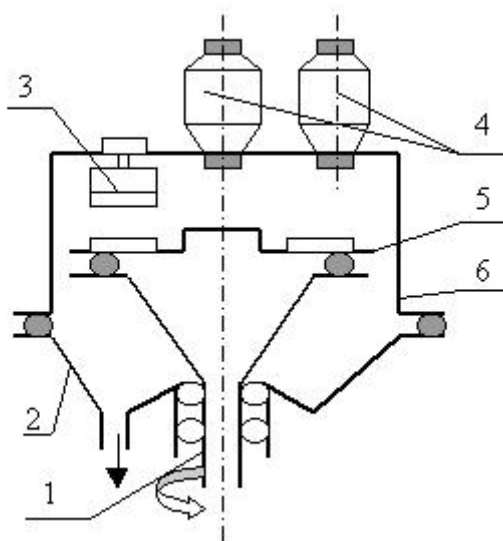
Схема установки травления, отмывки и сушки: 1 – полный ротор; 2 – днище камеры с отверстием; 3 – форсунка сушки; 4 – форсунки травления и отмывки; 5 – платформа с пластинами; 6 – съёмная крышка.
